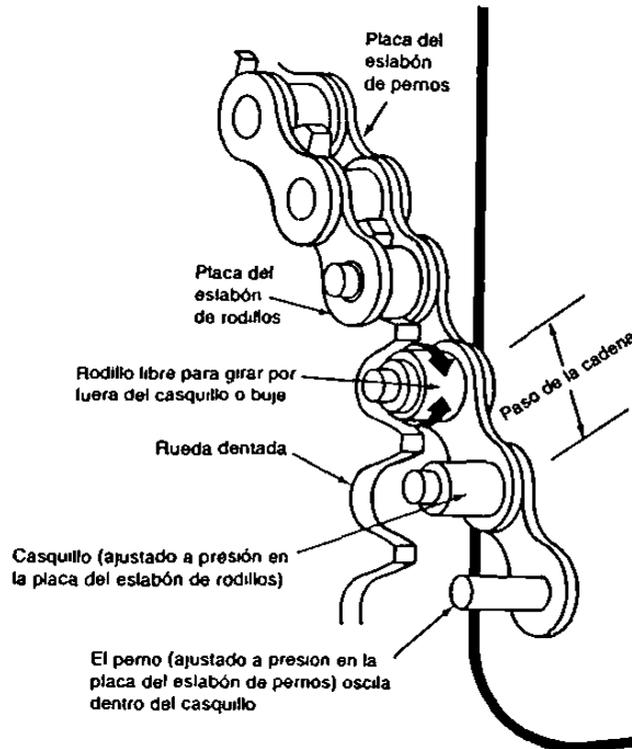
Montaje de los componentes de una cadena de rodillos sobre los dientes de una catarina.
